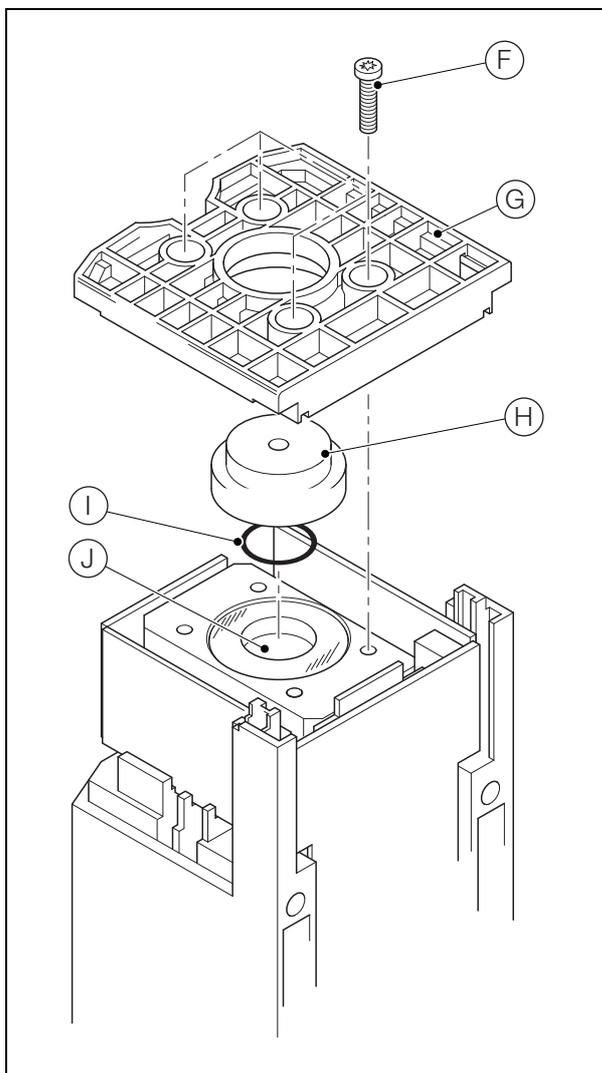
Desmontaje de la placa base de la célula de medida
